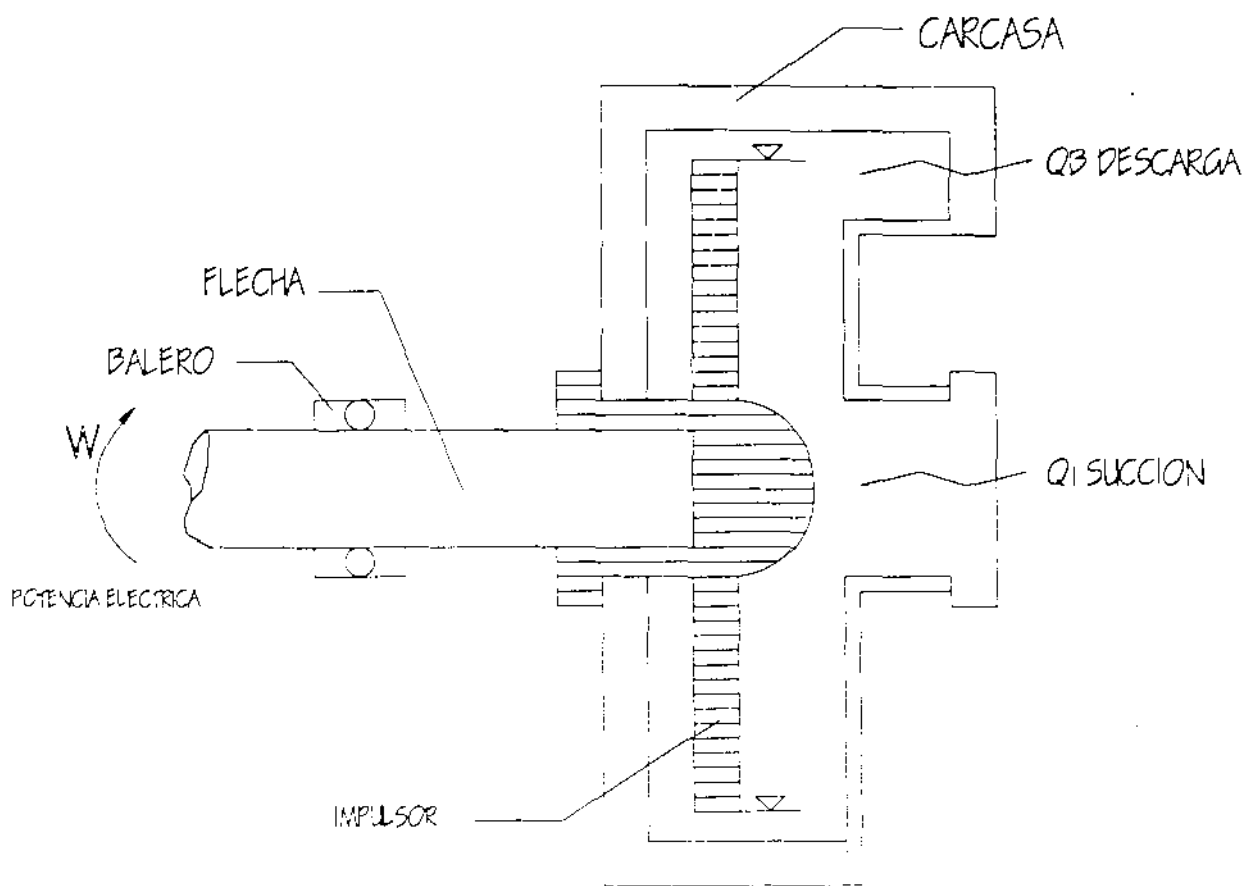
CORTE TRANSVERSAL DE BOMBA
